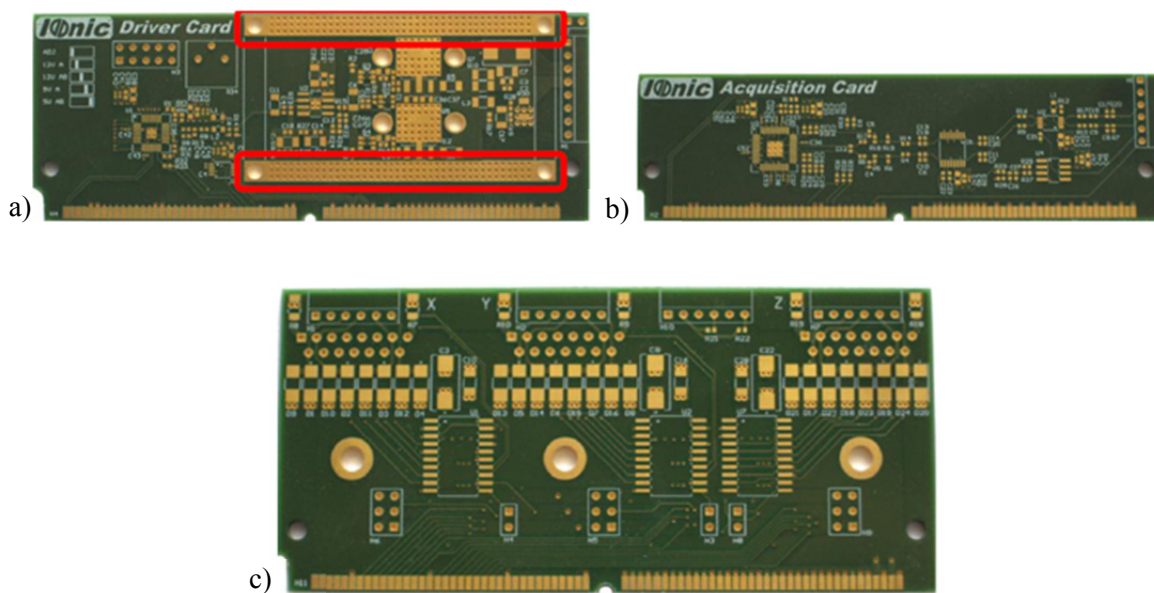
a) Placa de excitação da sonda IONic em PCB com dimensões 108x40 mm. b) Placa de aquisição de dados da sonda IONic em PCB com dimensões 108x30 mm. c) Placa de movimentação da sonda IONic em PCB com as dimensões 108x50 mm.
